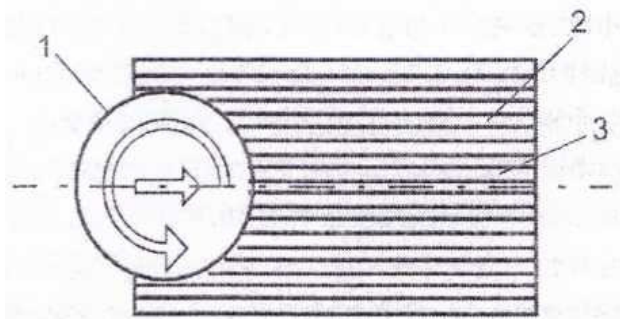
Схема СТП с поступательным перемещением вращающегося инструмента 1, погруженного в пакет пластин 2 из сплава 7075 с прокладками 3 из композитного материала Al – SiC (ось инструмента параллельна плоскости пластин)
